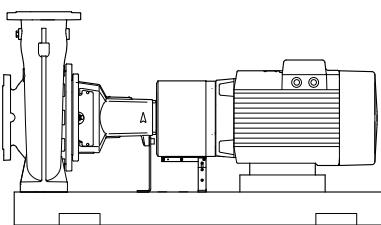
Vista esquemática de una bomba-motor N montada en una base
